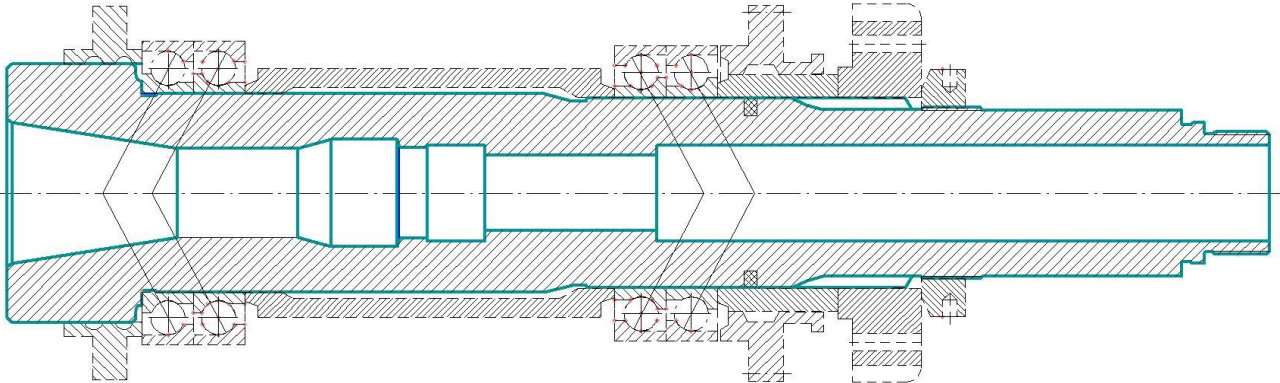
Конструктивна схема шпindelного вузла верстата СФ68ВФ4
